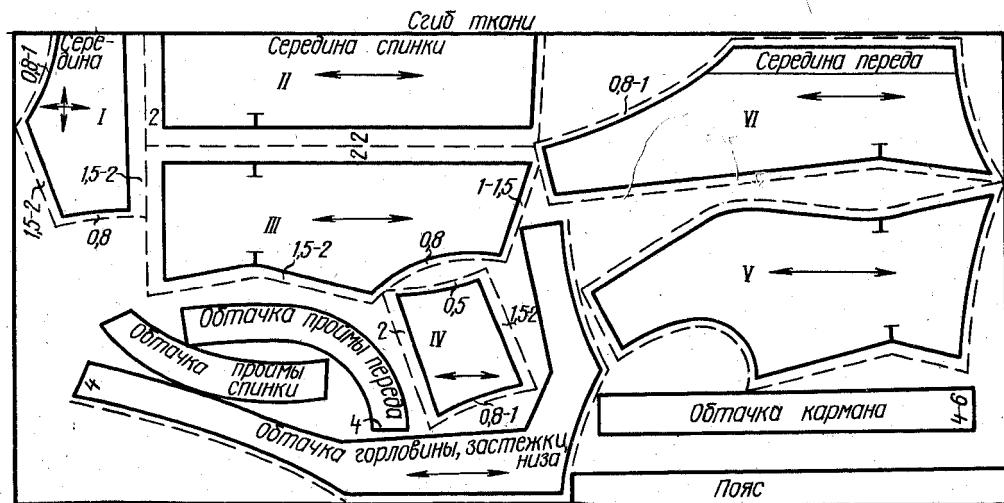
Раскладка выкроек на ткани и раскрой жилета
